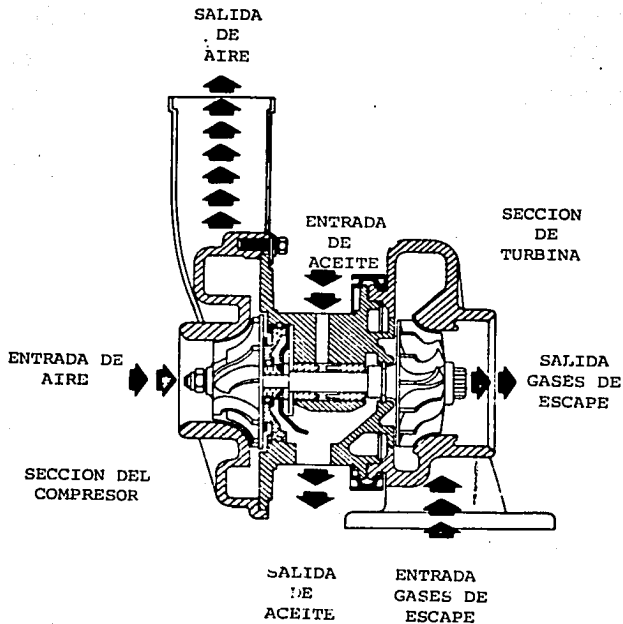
CORTE DE UN TURBOCARGADOR TIPICO.
